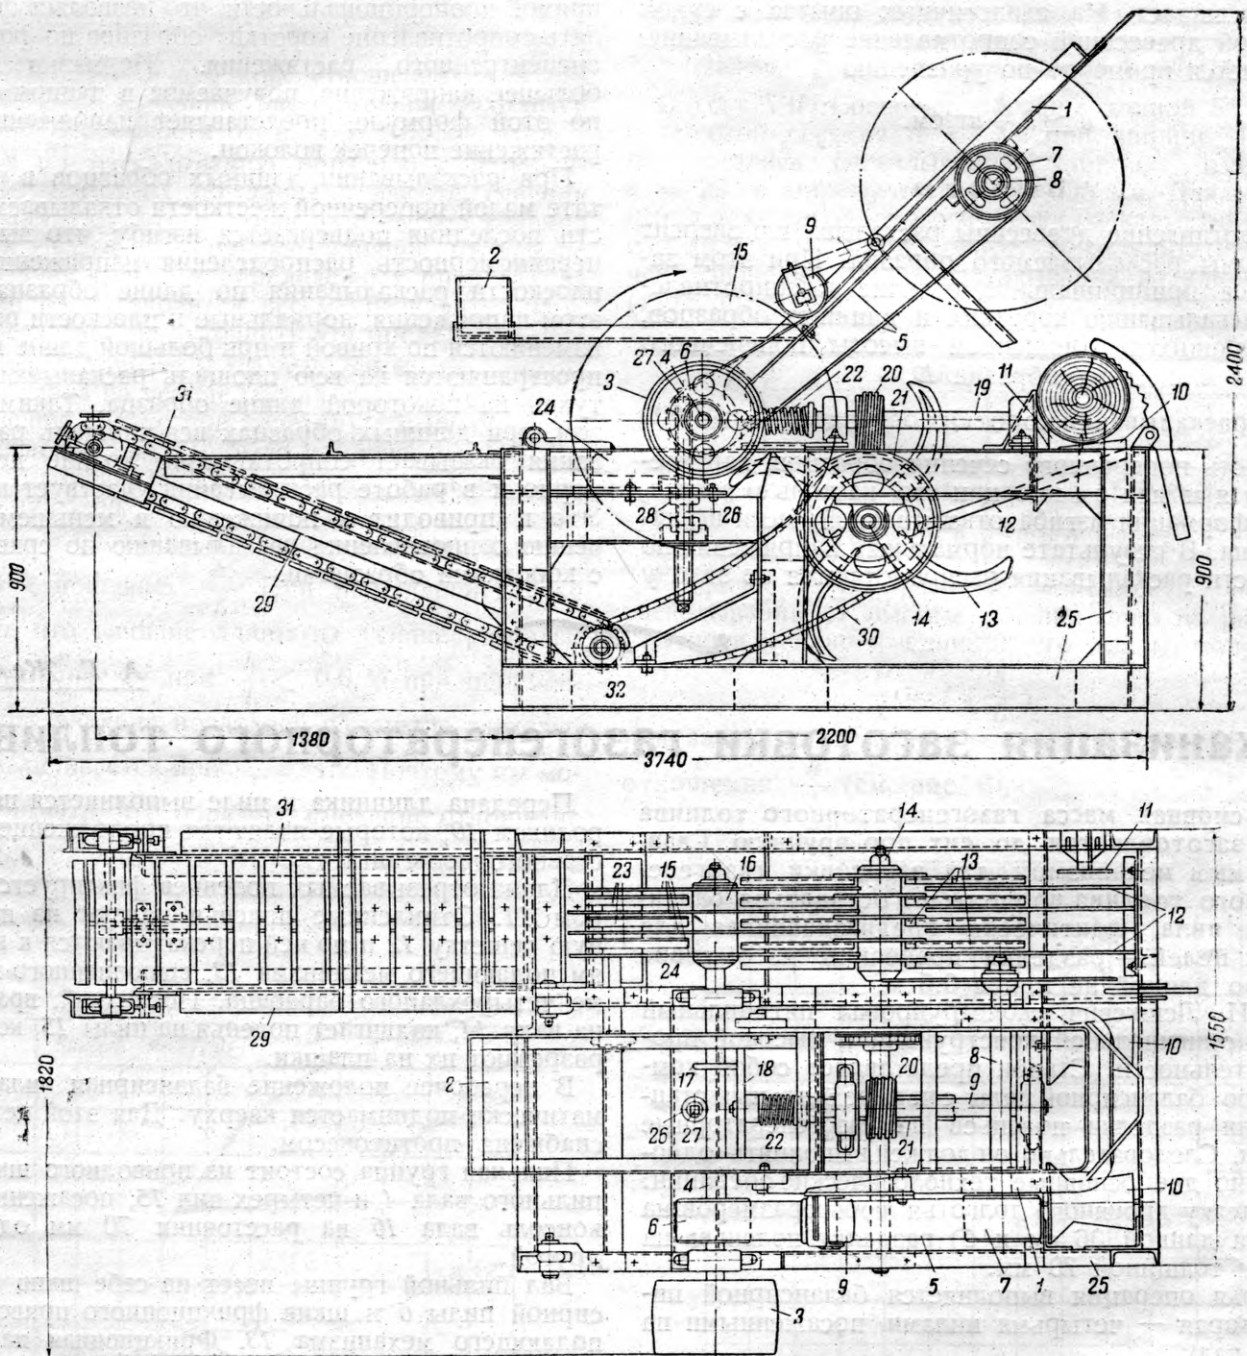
Пятипильный станок конструкции А. И. Лешкевича
